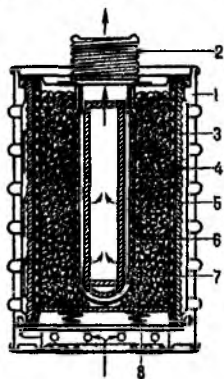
Разрез коробки пром. противогаза большого габарита (стрелками обозначено направление движения воздуха): 1 — корпус коробки; 2 — горловина коробки; 3 — ПАФ; 4 — большой перфорир. цилиндр; 5 — шихта; 6 — малый перфорир. цилиндр; 7 — противопылевый тампон; 8 — гру-жница.
